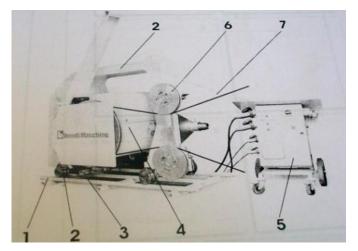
les paramètres principaux de machine fil diamanté [24]
